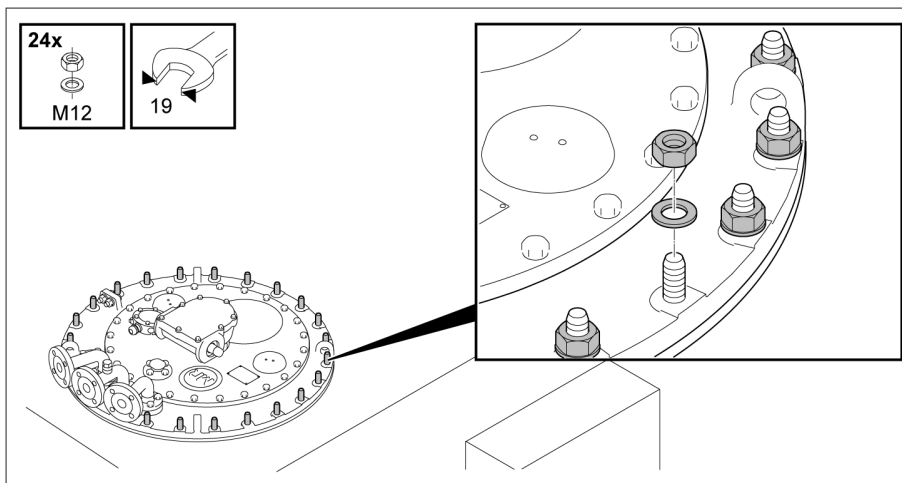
Cabeçote do comutador de derivação em carga com flange de montagem
